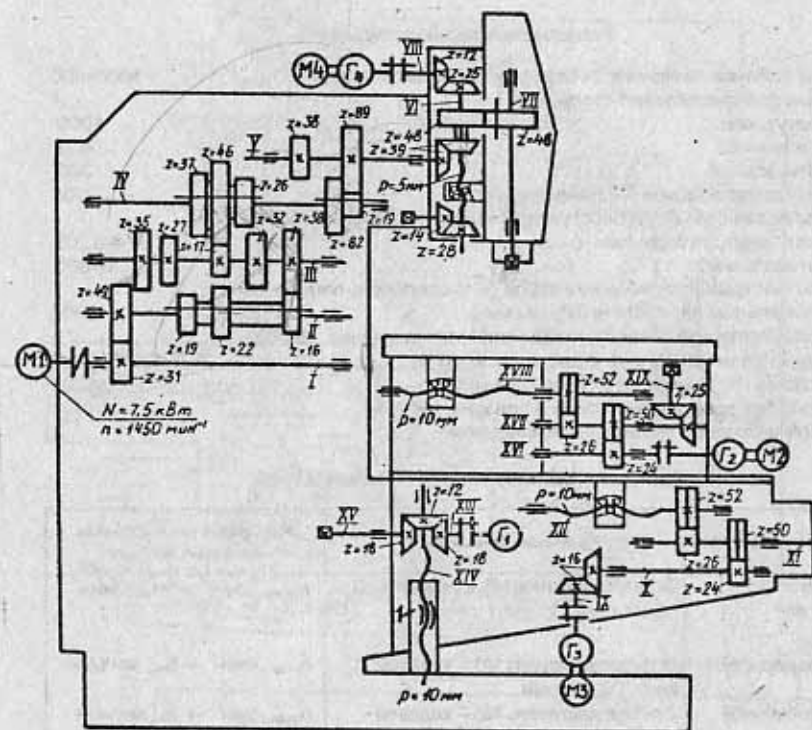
Кинематическая схема вертикально-фрезерного станка мод. 6Р13Ф3 с ЧПУ
